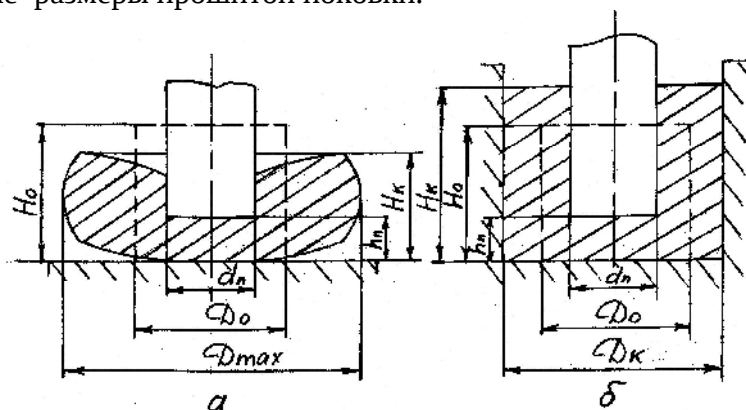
Характер изменения формы заготовки при открытой (а) и закрытой (б) прошивке.
